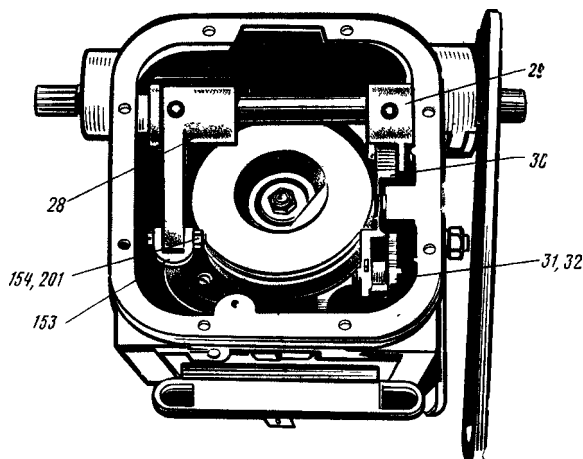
28 — перестановочный рычаг; 29 — рычаг изодрома; 30—промежуточный рычаг изодрома; 31—палец промежуточного рычага; 32—шплинт; 153—штанга сервомотора; 154—палец силового рычага; 201—шплинт
